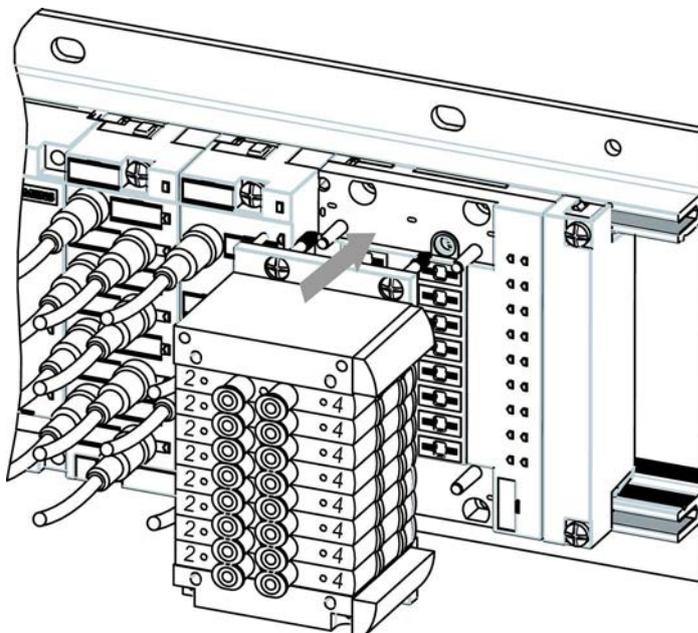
Montage der FESTO-Ventilinsel auf dem Pneumatik-Interfacemodul
